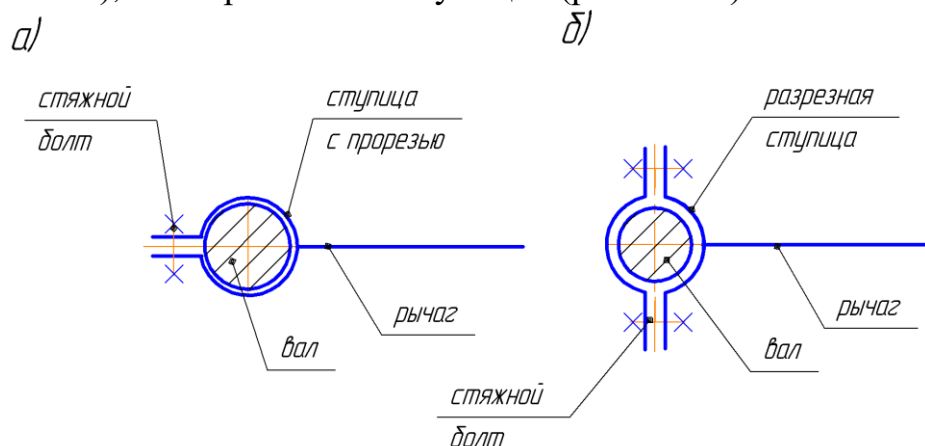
Схемы клеммового соединения: а – ступица с прорезью; б - с разрезной ступицей.
